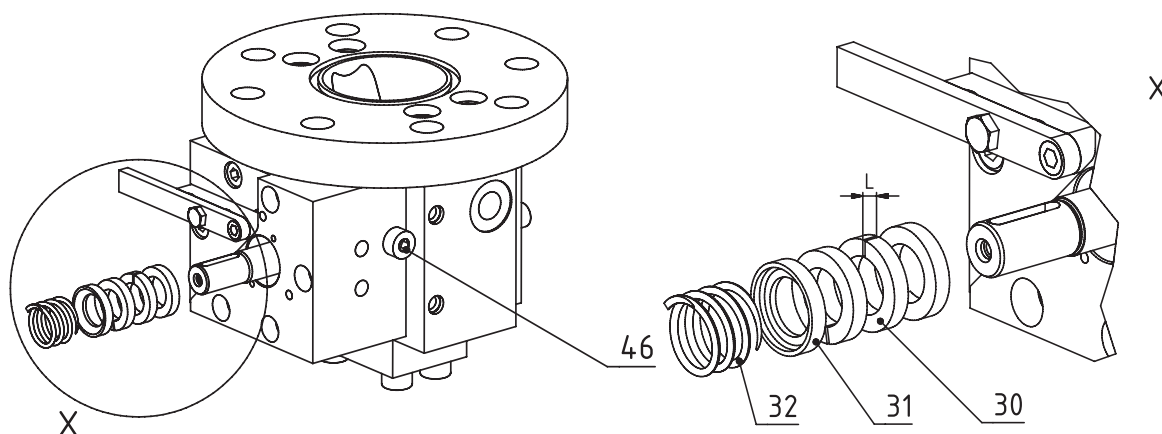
Задвиньте в корпус внутренние детали уплотнения вала;
